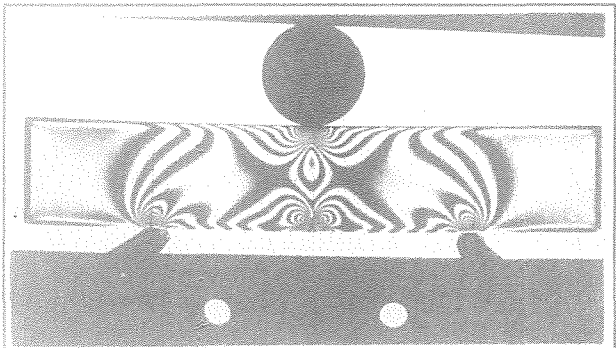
Isocromáticas de soldadura a tope con falta de penetración en raíz, sometida a flexión.
